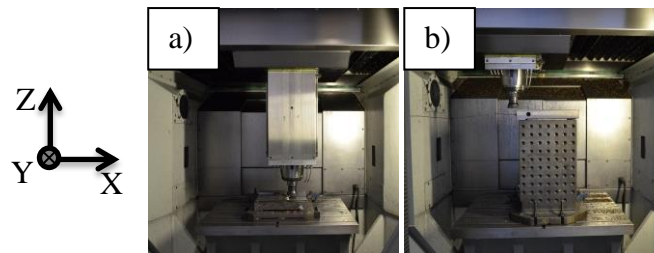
Configurations d'usinage : a) usinage en bas, b) usinage en haut
